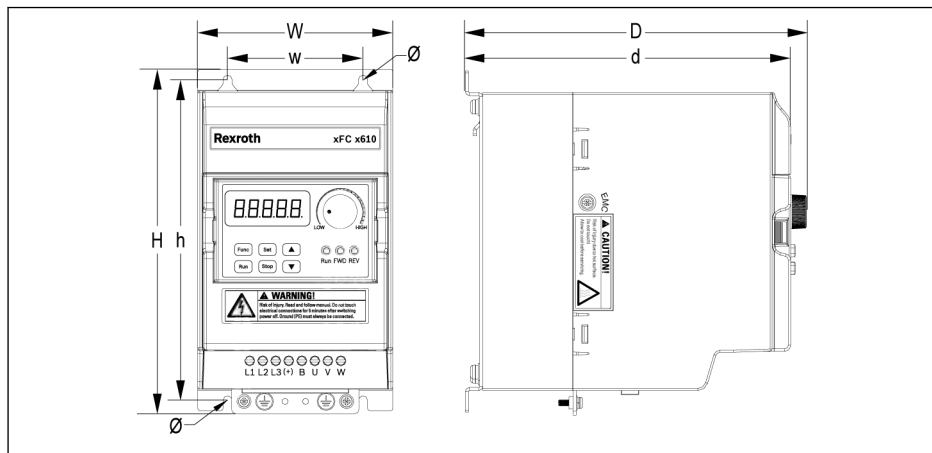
Размерный чертеж VFC x610 OK40...4K00
